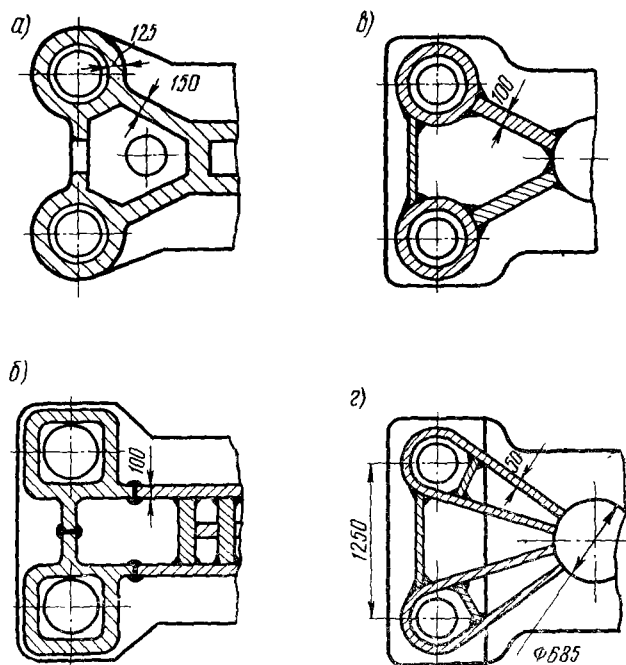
Различные конструктивные решения изготовления поперечин пресса усилием 4500 Т:
